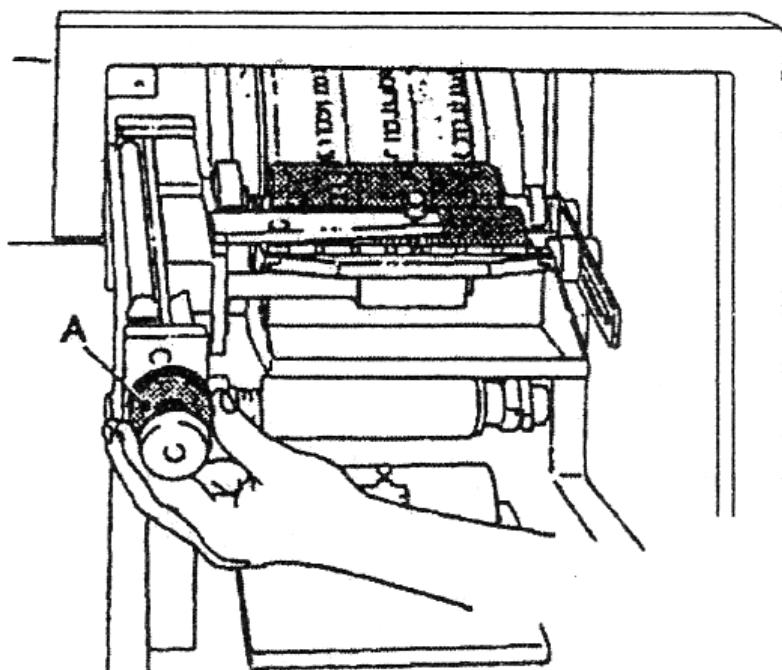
Регулировка давления между формой и запечатываемым материалом
